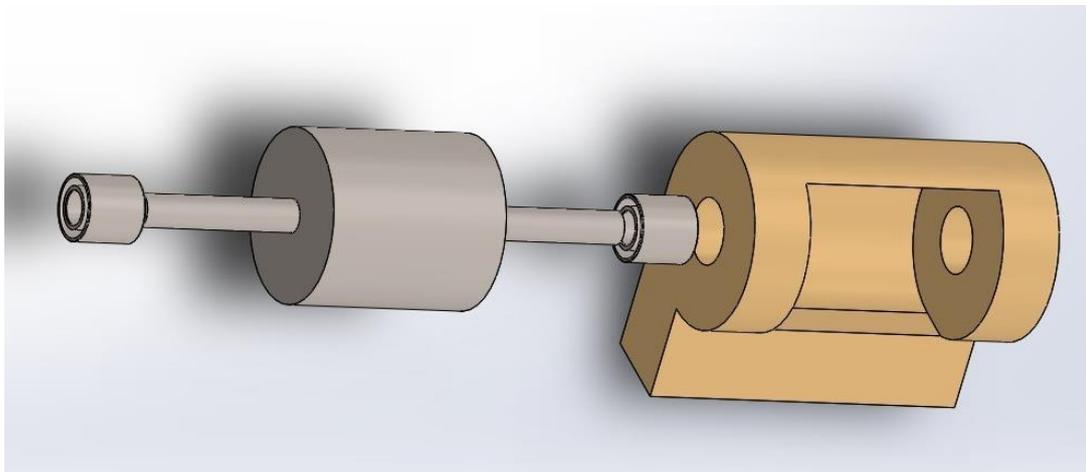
Diseño rodillo y soporte del mismo explosionados
